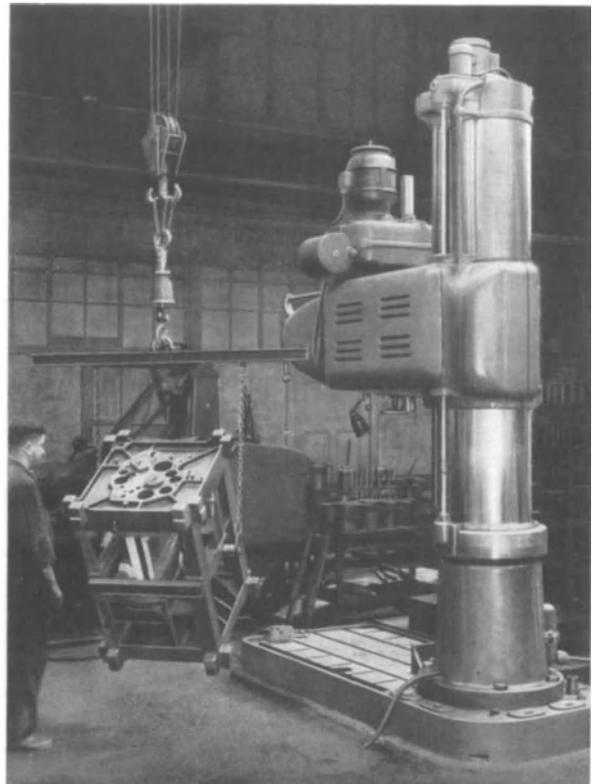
Wenden einer Bohrvorrichtung mit dem Kran
